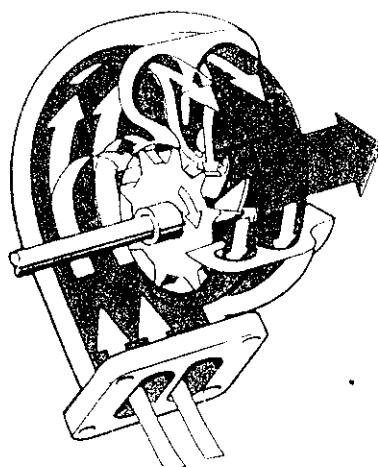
Diesel Motorlar İçin Dizayn Edilmiş Bir Turbo Şarj Grubu
